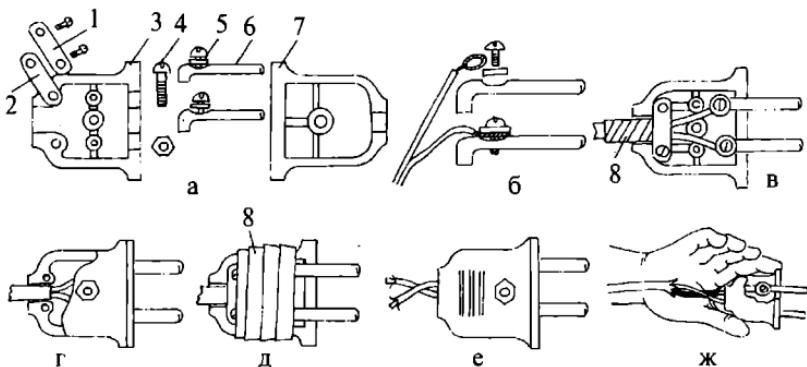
Монтаж и ремонт вилки с цельными штифтами и разборным корпусом: а — разборка вилки; б — зачистка жил, загиб их в петли и соединение винтами со штифтами; в — установка штифтов в углубления основания корпуса и закрепление проводников скобой и прокладкой; г — соединение крышки и основания корпуса центральным винтом; д — замена крышки корпуса обмоткой из изоляционной ленты; е — скручивание проводников до подсоединения к электроприбору; ж — укорочение проводников; 1 — изолирующая прокладка; 2 — металлическая скоба; 3 — основание корпуса; 4 — винт центральный; 5 — шайба; 6 — штифт цельный; 7 — крышка корпуса; 8 — изоляционная лента
